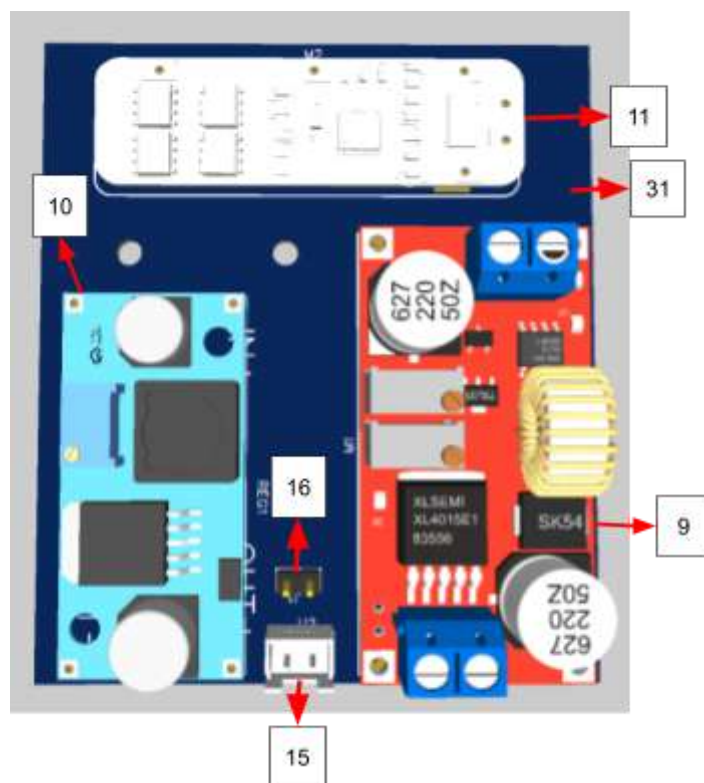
PCB da placa de alimentação com componentes soldados
